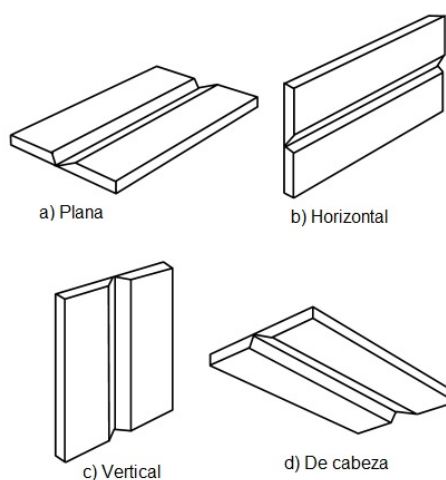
Posiciones básicas para el proceso de soldadura por arco eléctrico (21).
